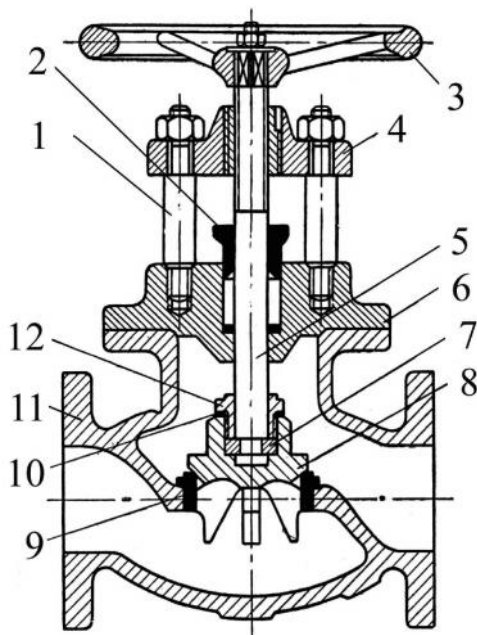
Клапан проходной запорный: 1 – колонка; 2 – нажимная втулка; 3 – маховик; 4 – поперечина; 5 – шток; 6 – крышка; 7 – кольцо; 8 – тарелка; 9 – седло; 10 – шайба; 11 – корпус; 12 – гайка
